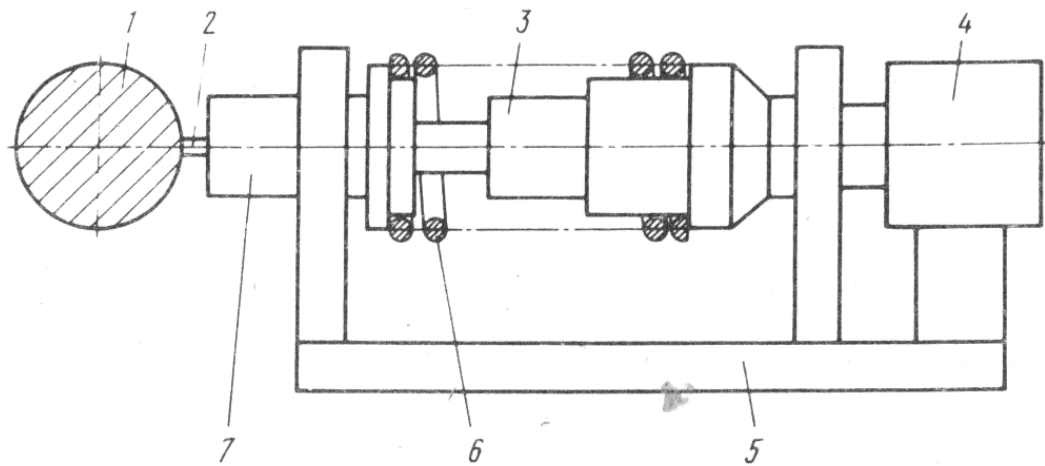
1 Принципова схема установки для фрикційного латунування валів.
